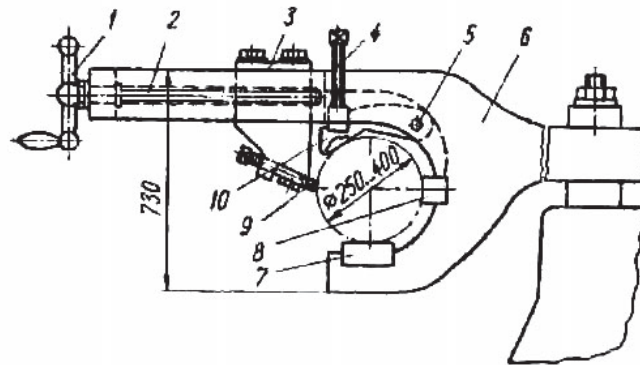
Пристрій для проточування шийок колінчастого вала під люнет
